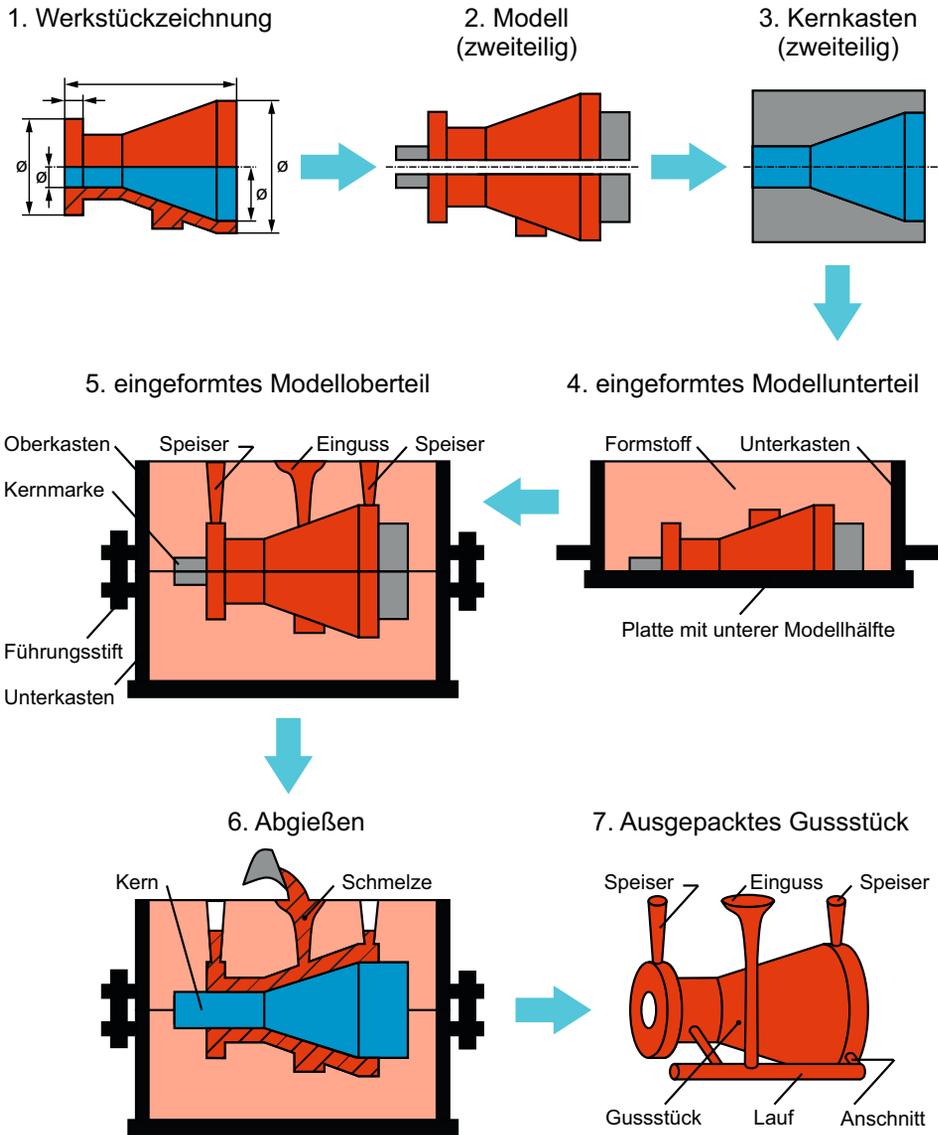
Verfahrensablauf der Gussteilfertigung mittels Handformerei
